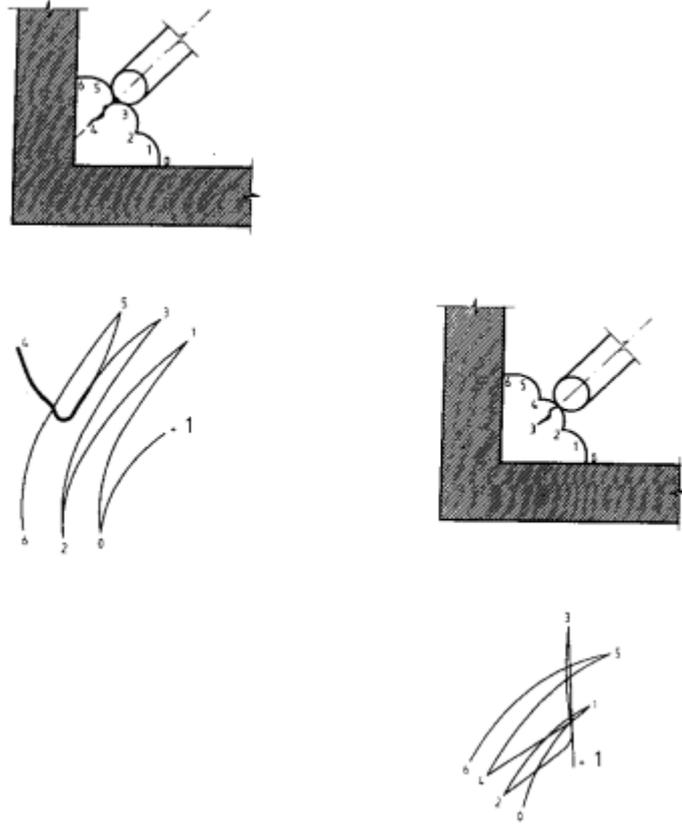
焊缝帽检查之际产生的典型缺陷信号
